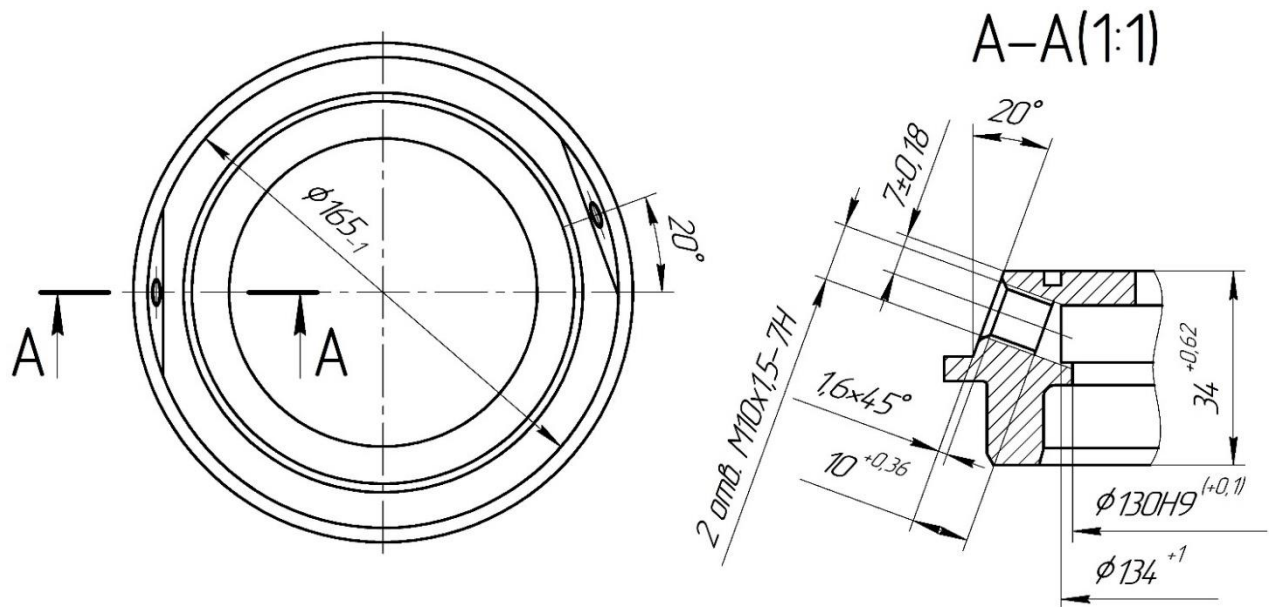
Розташування двох «лисок» на поверхні корпусу
